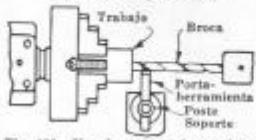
Uso de un porta-herramientas para estabilizar la punta de la broca
